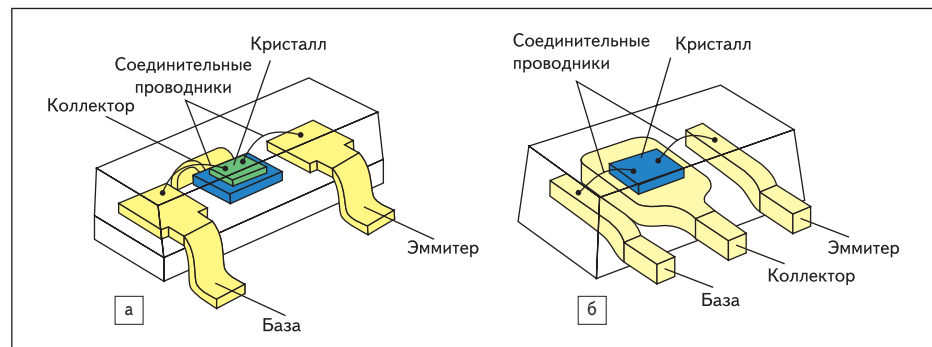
Конструкции транзисторных корпусов: а) SOT-23; б) SOT-89
